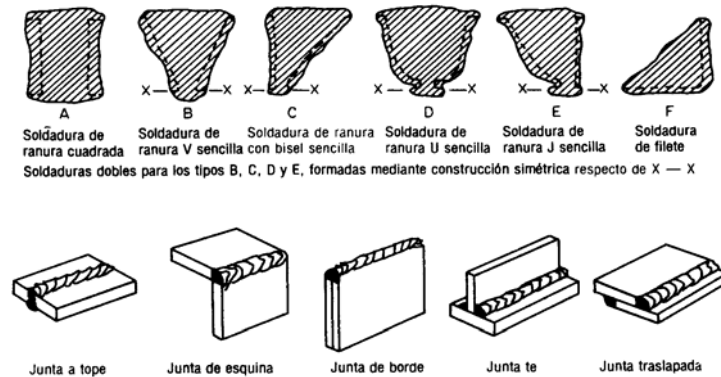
Algunos tipos de soldaduras (arriba) y de juntas (abajo).
